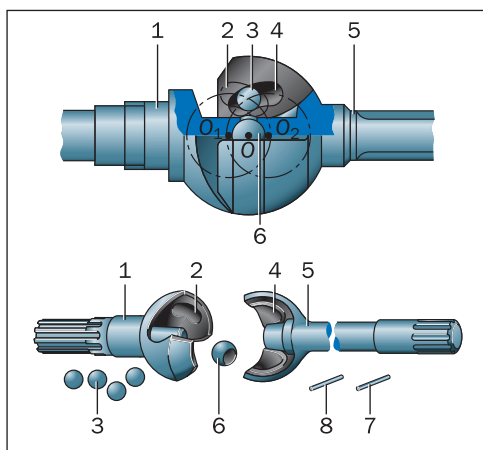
Шарнир с делительными канавками типа «Вейс»: 1, 5 — валы; 2, 4 — кулаки; 3 — шарики; 6 — центрирующий шарик; 7, 8 — фиксирующие штифты
